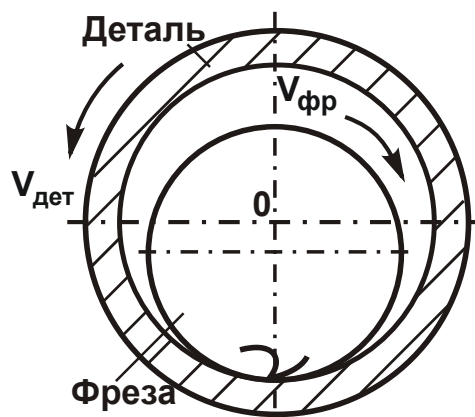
Схема фрезерування отвору кінцевою фрезою
